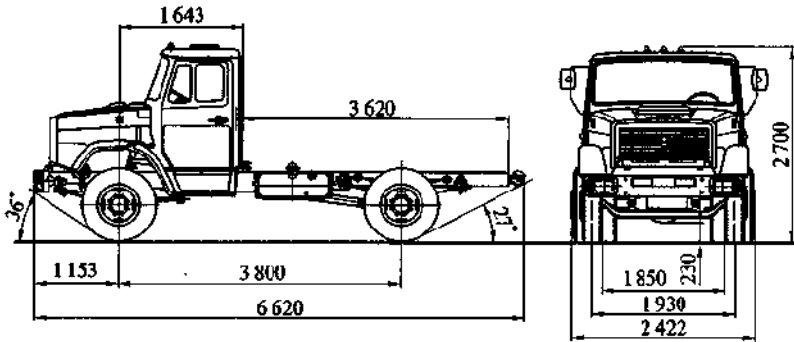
Габаритні розміри ЗІЛ-433362
